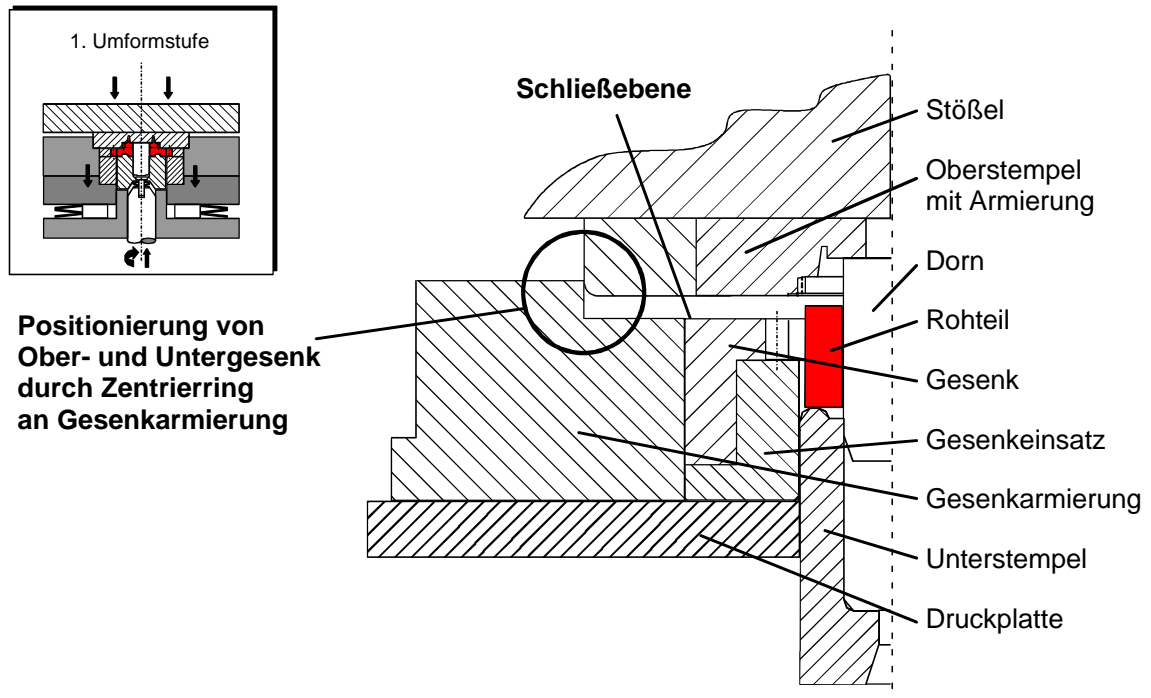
Positionierung der Werkzeugelemente Oberwerkzeug und Matrize zueinander
